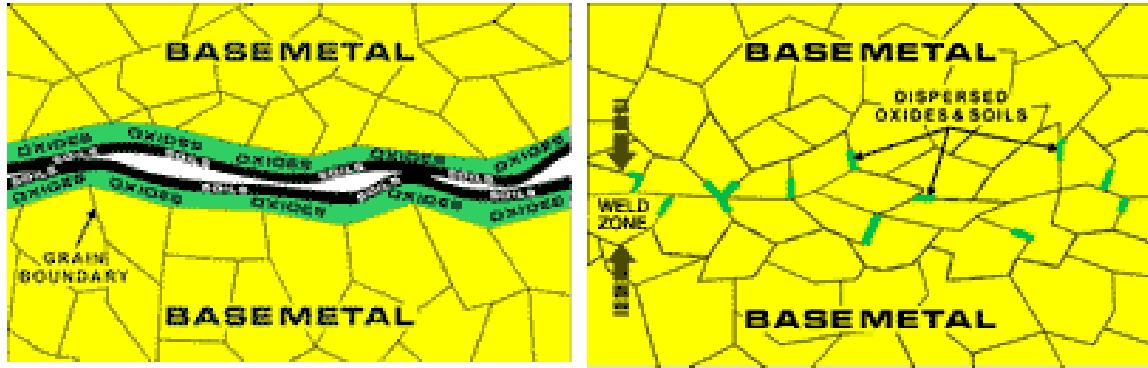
a) Antes da soldagem. b) Depois da soldagem.
